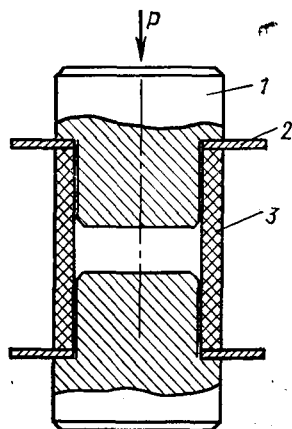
Схема приспособления для термокомпрессионной пайки керамики с металлом
